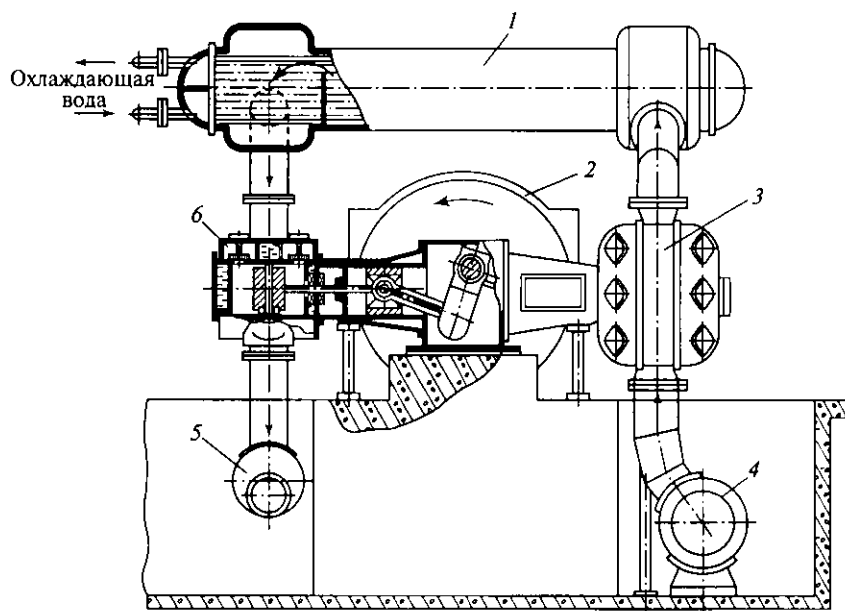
Схема двухступенчатого оппозитного компрессора типа ВМ:
